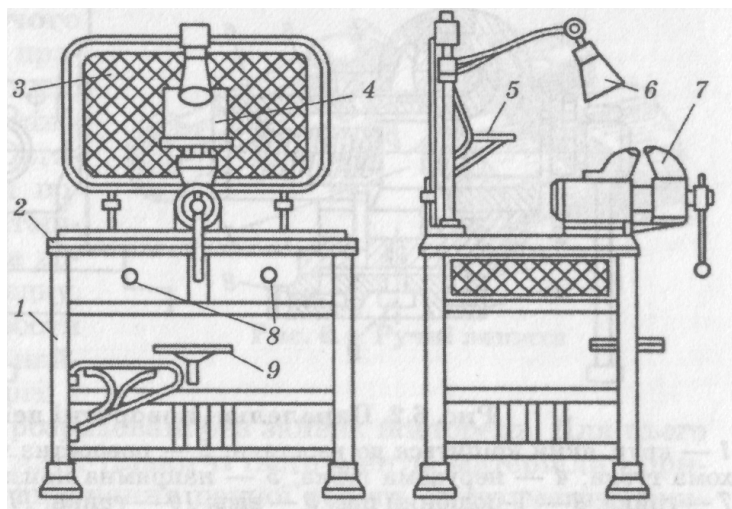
Одномісний верстак: 1 — каркас; 2 — стіл верстака; 3 — запобіжна сітка (екран); 4 — планшет для креслення; 5 — поличка для контрольно-вимірювальних приладів; 6 — світильник; 7 — лещата; 8 — ящики; 9 — сидіння
